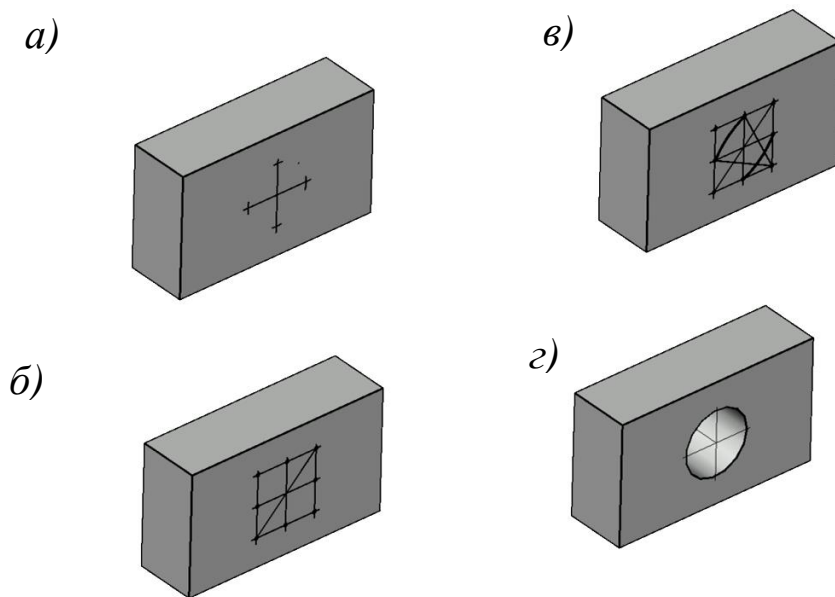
Построение изометрической проекции детали с цилиндрическим отверстием
